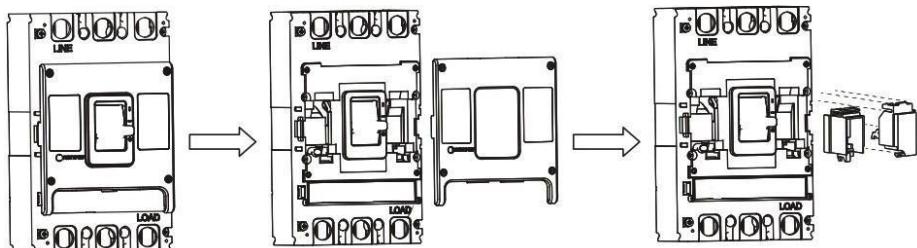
Схема установки аксессуаров внутрь корпуса аппарата
